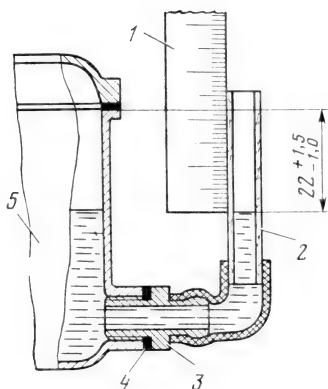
Проверка уровня топлива в поплавковой камере карбюратора:
